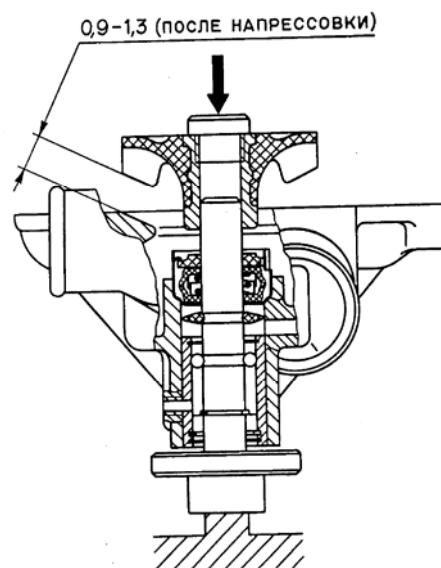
Напрессовка крыльчатки водяного насоса
